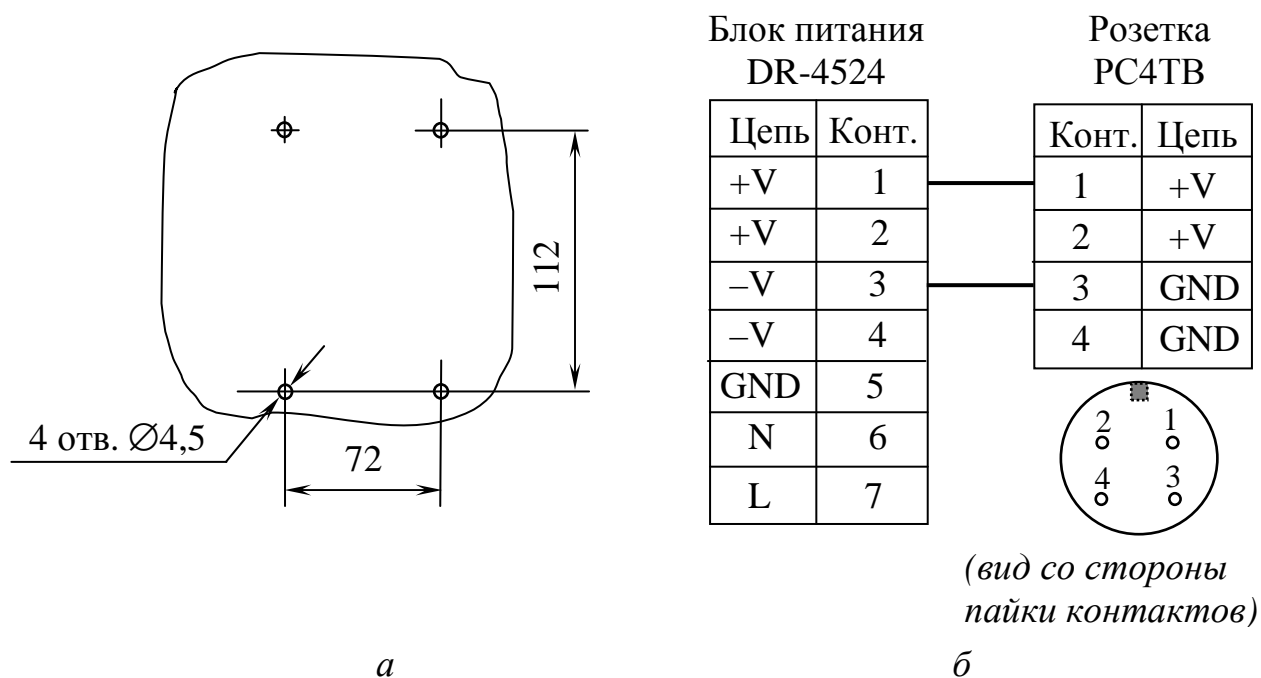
Расположение отверстий для крепления источника питания ИП-1002 и схема соединений кабеля
